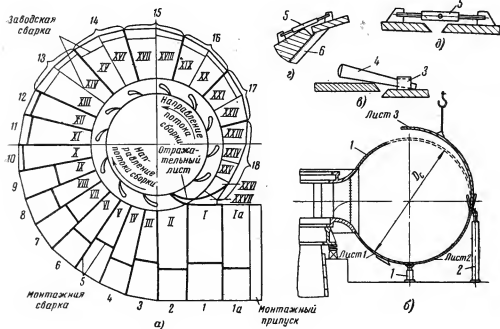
Сборочная схема сварной спиральной камеры.
